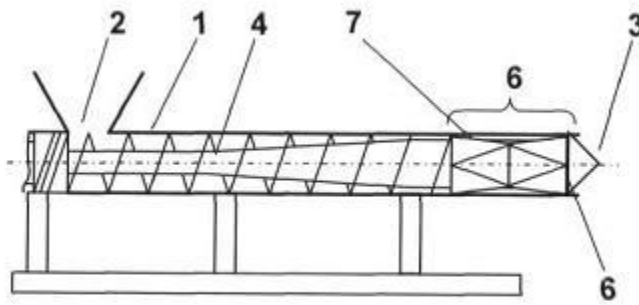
Поздовжній переріз черв'ячної машини
